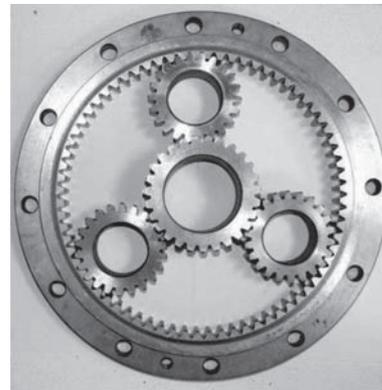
Зубчатые колеса из ВЧТГ, для бортового редуктора УЭС 2-250
